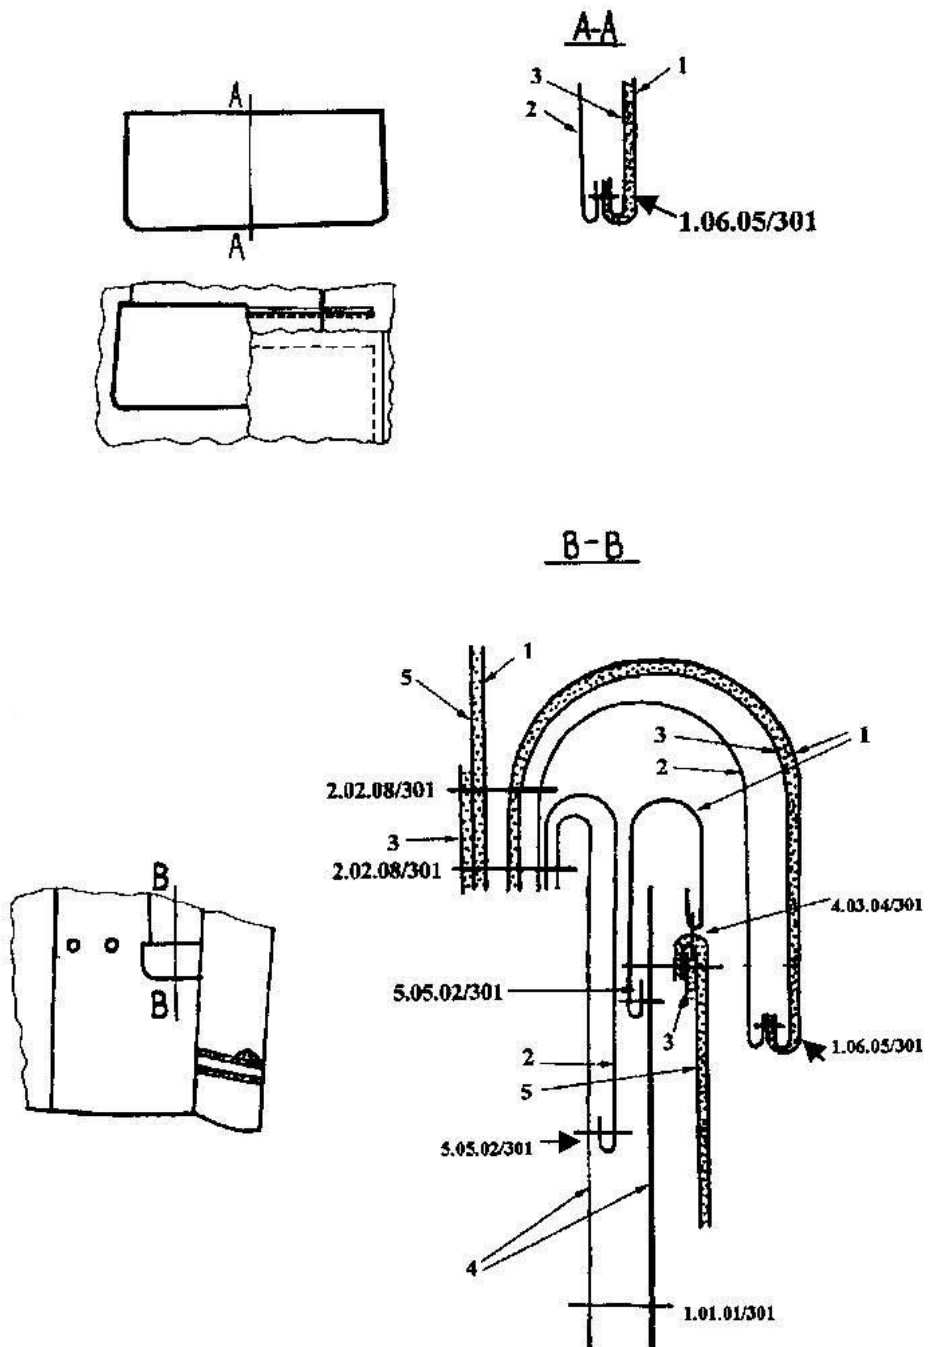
Klejenie boczaków oraz rękawów wierzchnich i spodnich
